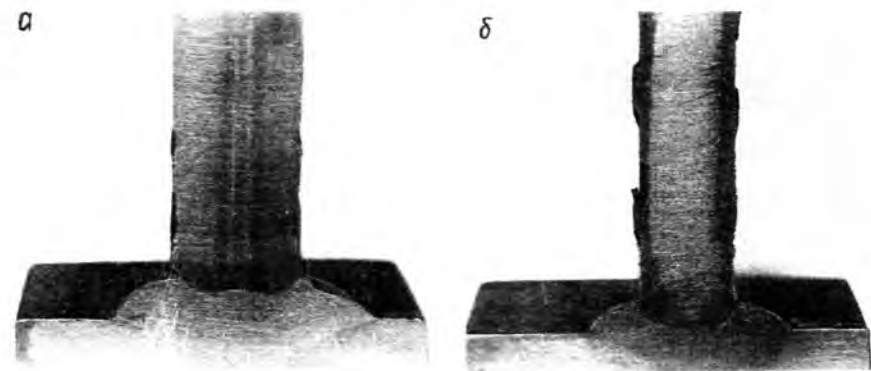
Макрошлифы сварных соединений, полученные при использовании нового состава сварочного флюса
